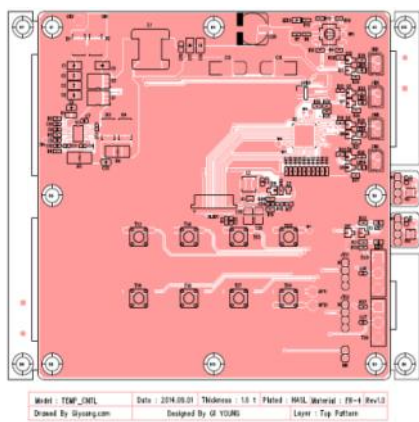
OLED controller 기본 회로 구성도로 제작한 PCB 기판
